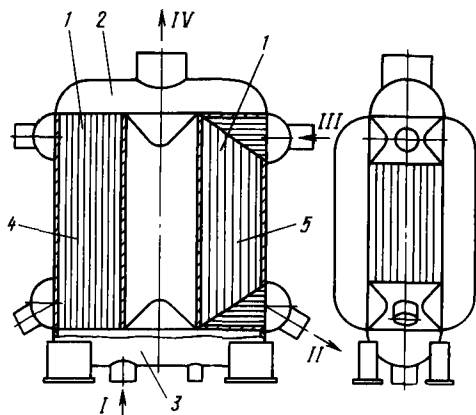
Вертикальный пластинчато-ребристый конденсатор-испаритель:
